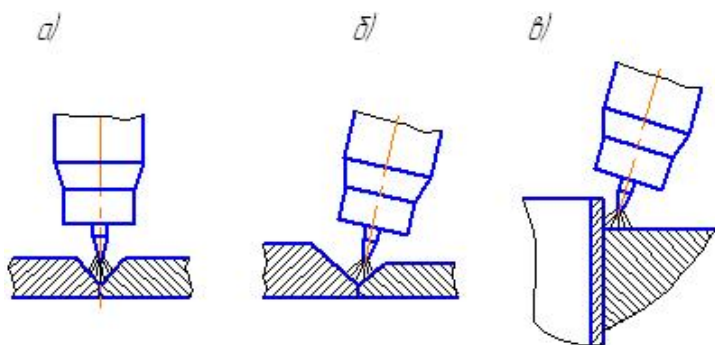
Влияние вида сварного соединения на наклон электрода
